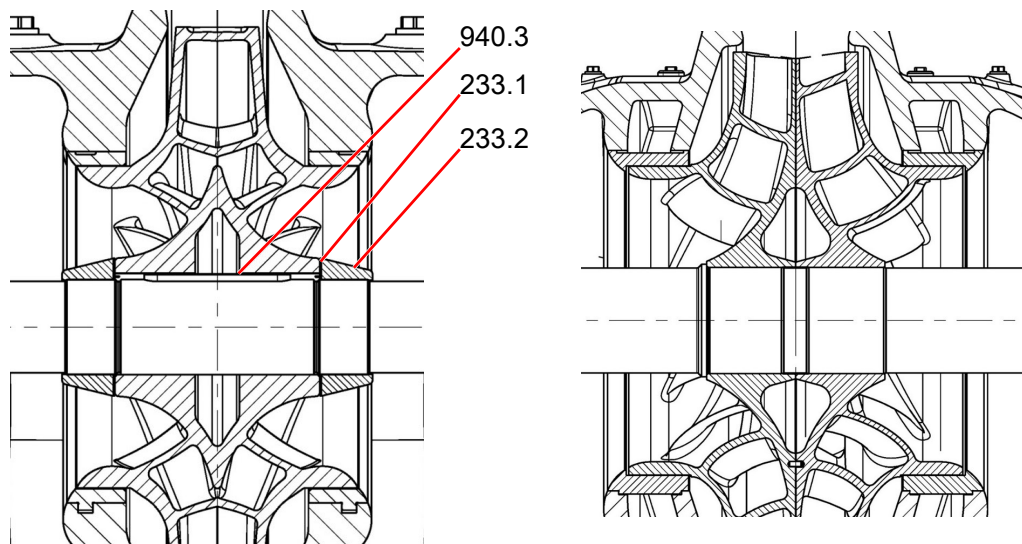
Крепление рабочего колеса при помощи призматической шпонки и гайки вала (слева) и прессовой посадки (справа)
